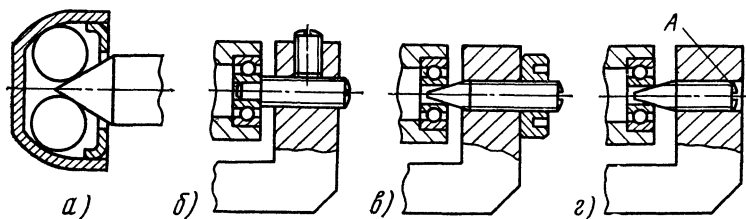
Примеры конструкций цапф поворотной ножки тонарма.
